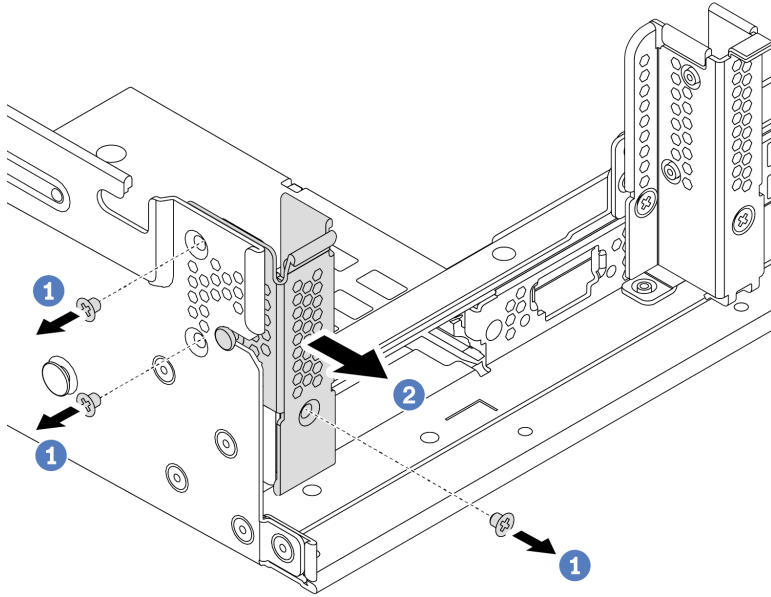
Installazione della staffa posteriore A1 per il montaggio a parete
